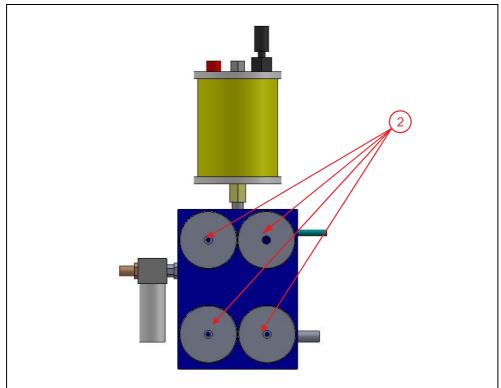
Minimalmengenschmiergerät mit Magneten befestigen
